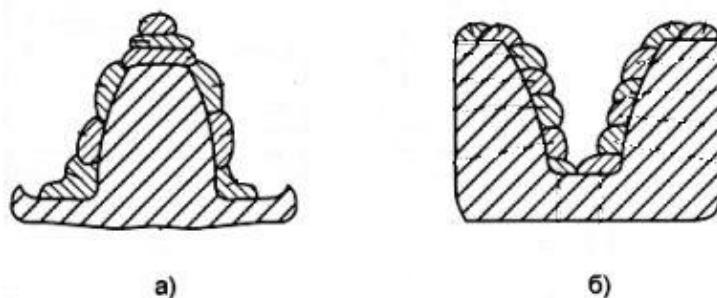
Наплавлення зубів (а – вершина зуба; б – впадина зуба)
